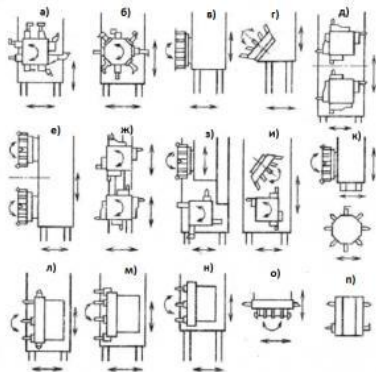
Схемы конструктивного исполнения револьверных головок токарных станков
